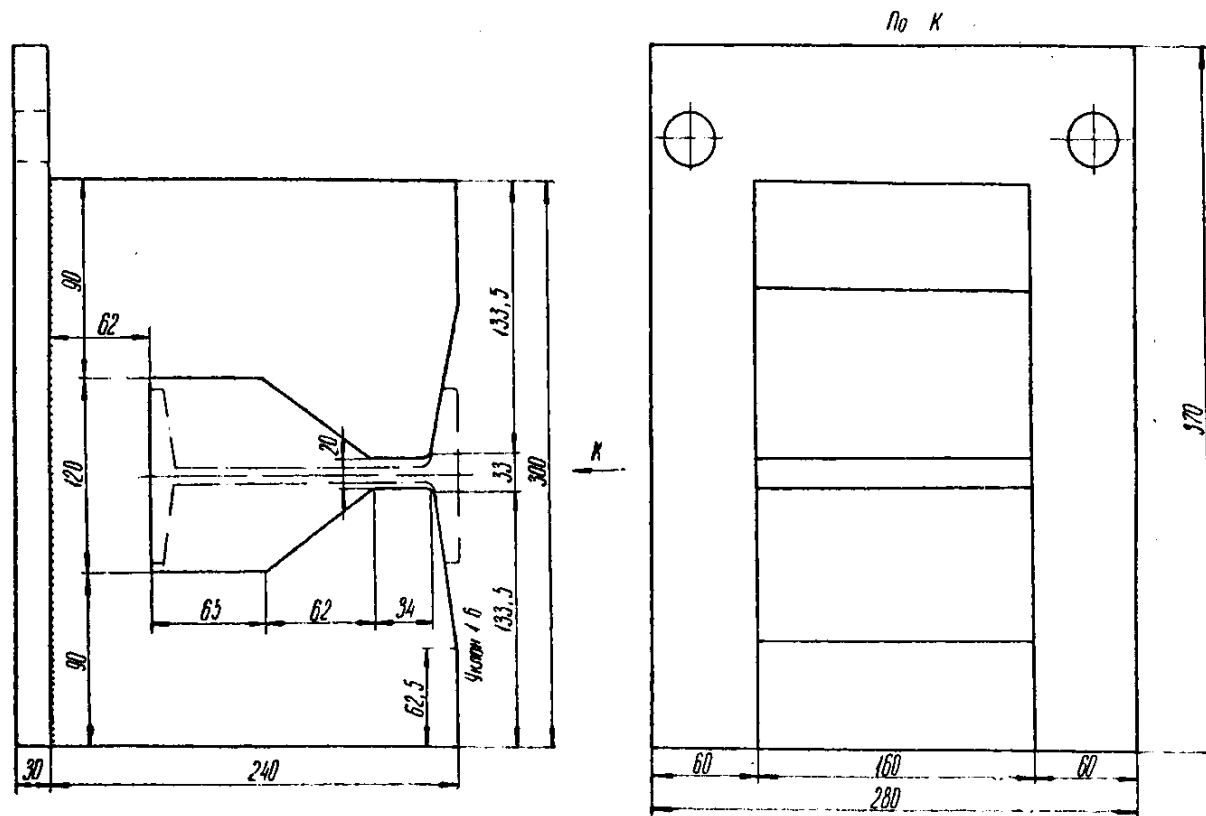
Приспособление, крепящееся к ползуну кулачкового пресса.
